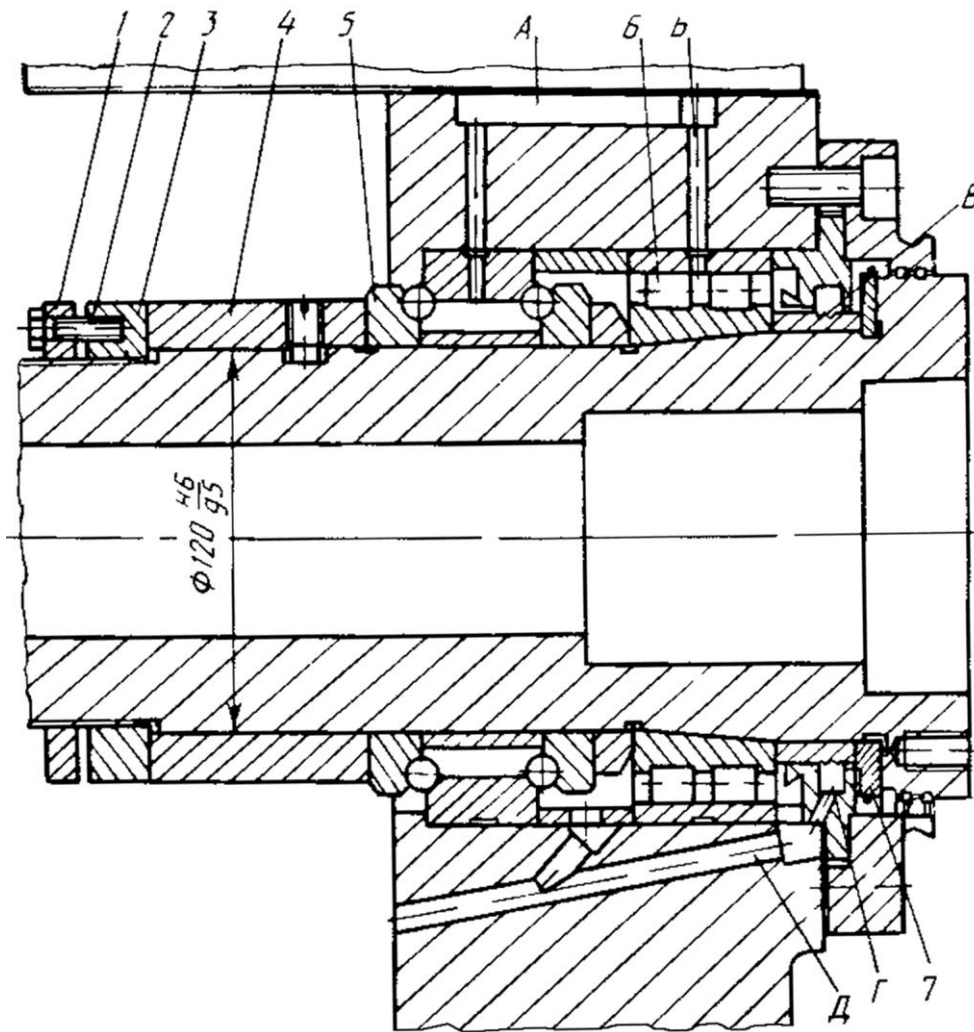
Передня опора та кінець шпинделя фрезерно-розточувального верстата з ЧПК
